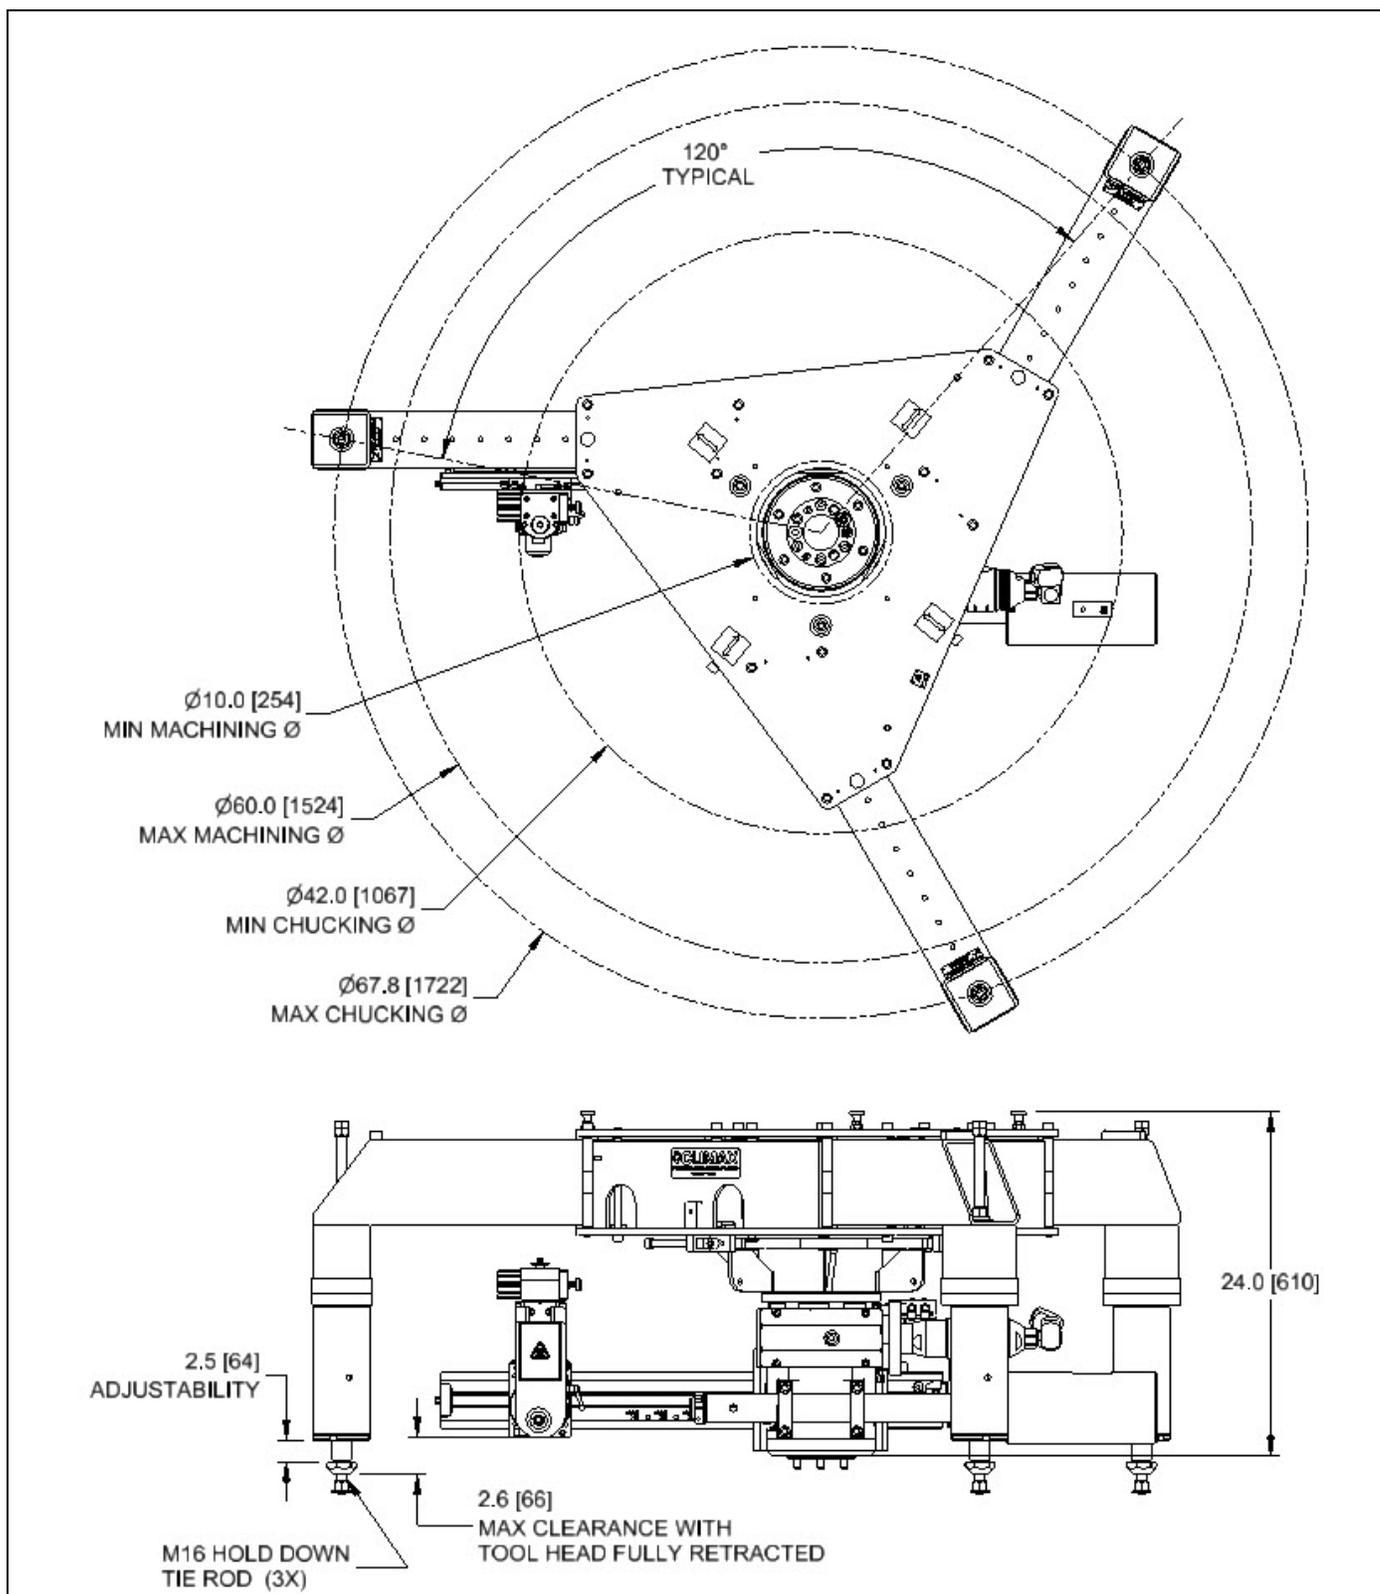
DIMENSIONES DEL ENSAMBLAJE DE AMARRE EXTERIOR FF6300
